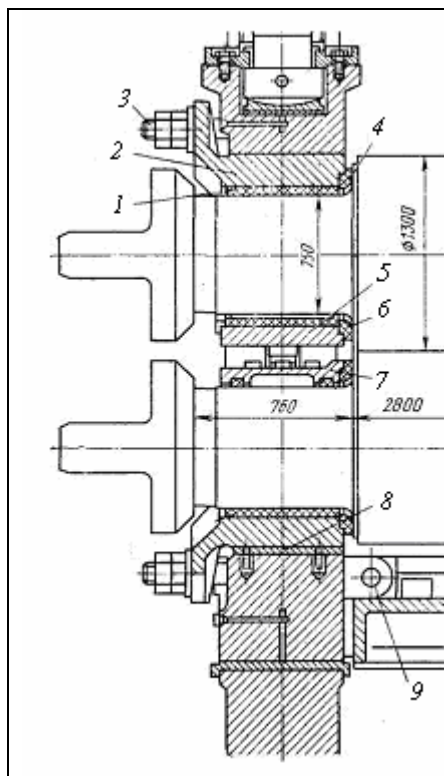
Подшипниковый узел блюминга: 1-текстолитовый вкладыш; 2-кассета; 3-болт; 4-текстолитовые фланцы; 5-подвеска; 6-текстолитовый вкладыш; 7-крышка; 8-сменные прокладки; 9-проушина
